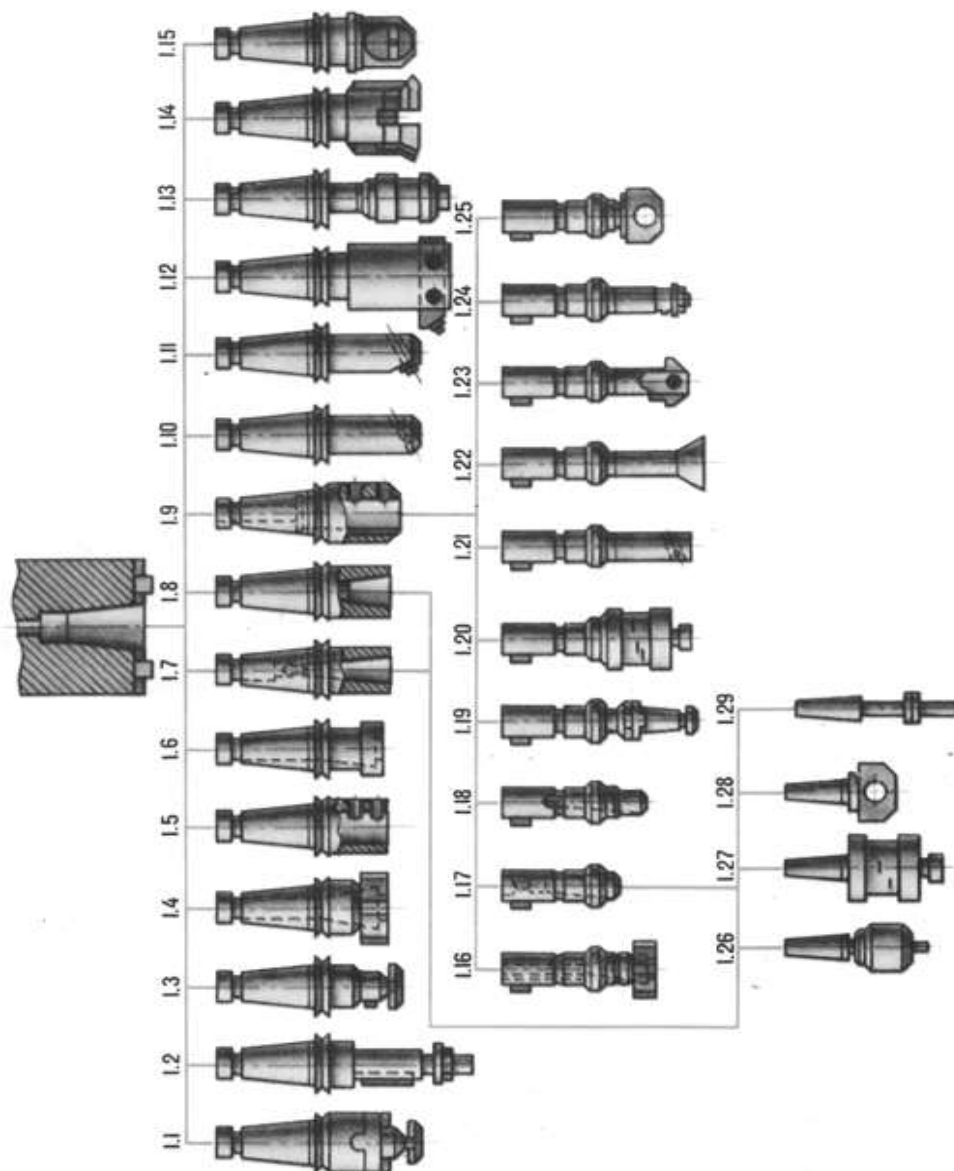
Система допоміжного інструменту для модулів обробки свердлильно-фрезерно-розточний групи
